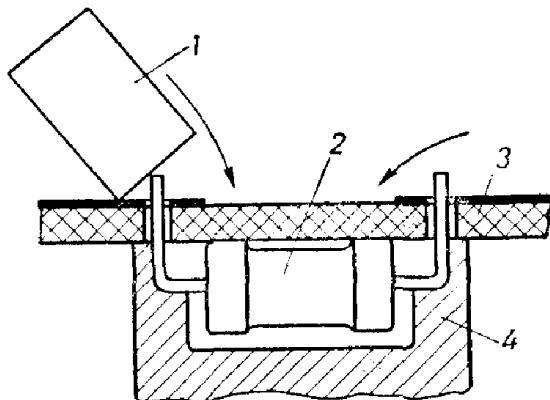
Способ закрепления навесных деталей на плате печатной схемы подгибкой выводов:
